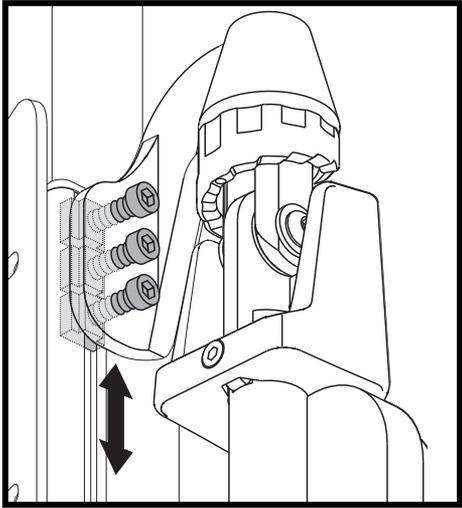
Réglage en hauteur des accoudoirs Cantilever sur inclinaison motorisée
